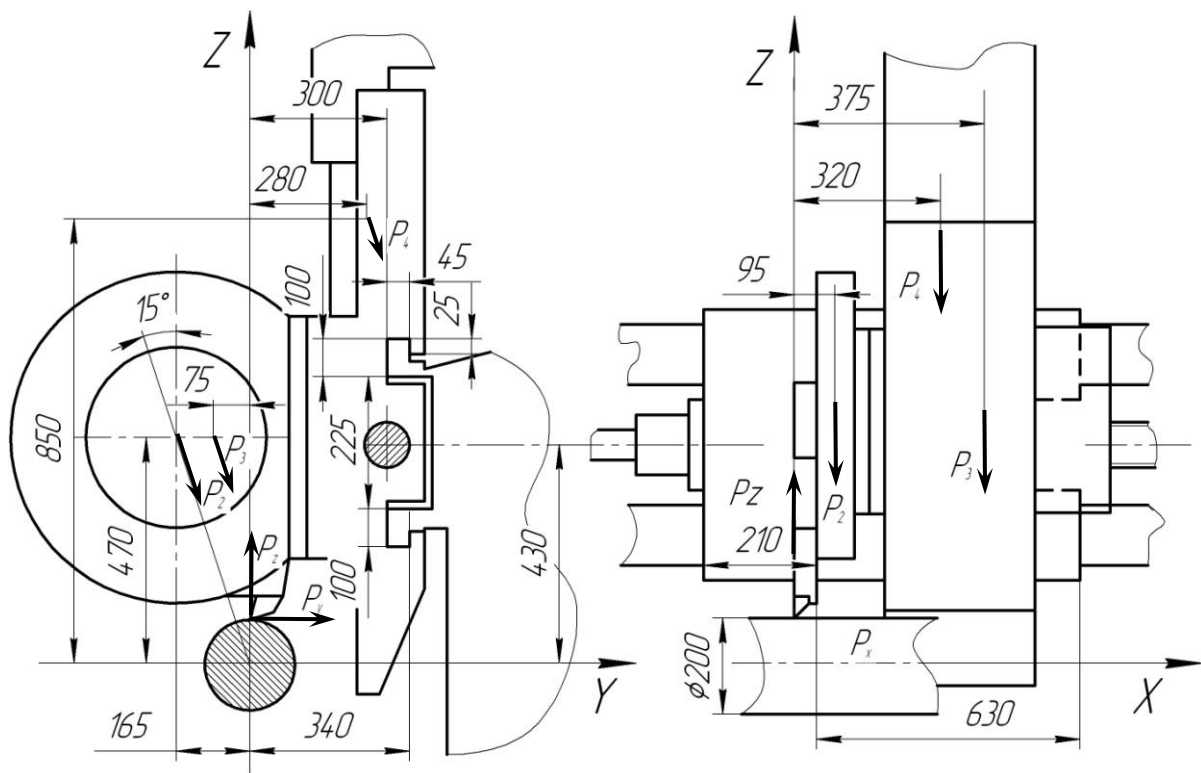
Розрахункова схема напрямних ковзання токарно-револьверного верстата з ЧПК
